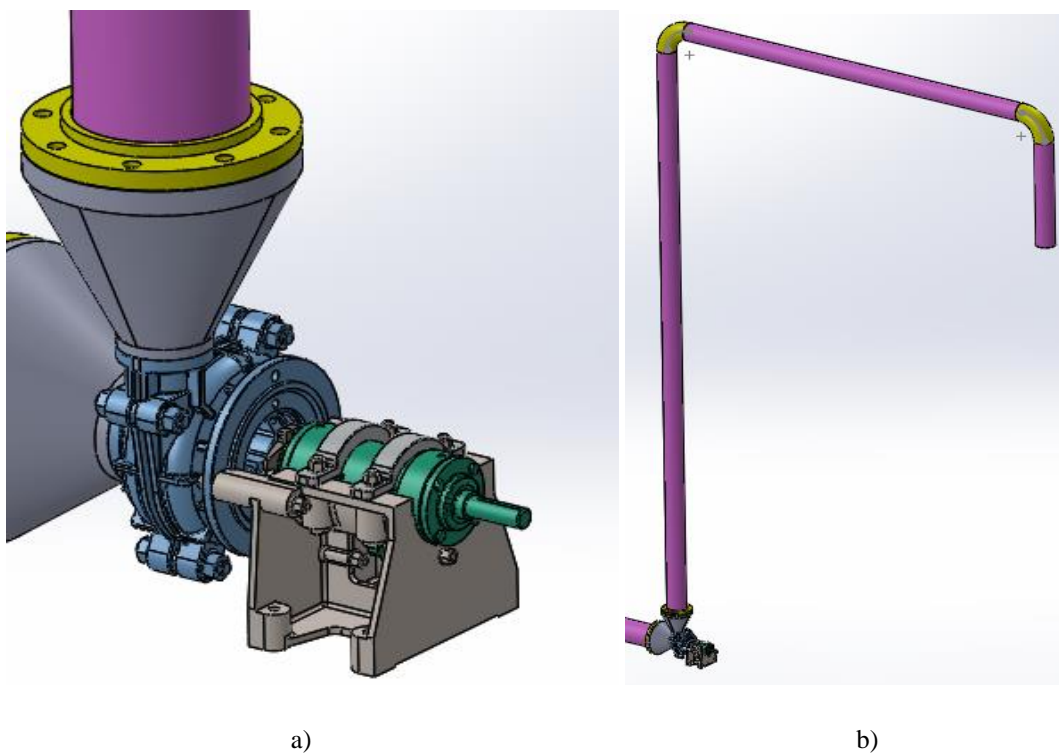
a) Brida de soldadura 8 plg; b) Diseño de tubería de descarga.
